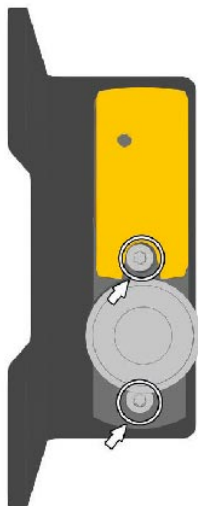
Prozesszuhaltung auf Montageplatte anbringen und Schrauben M6 x 25 mm Torx festziehen.
